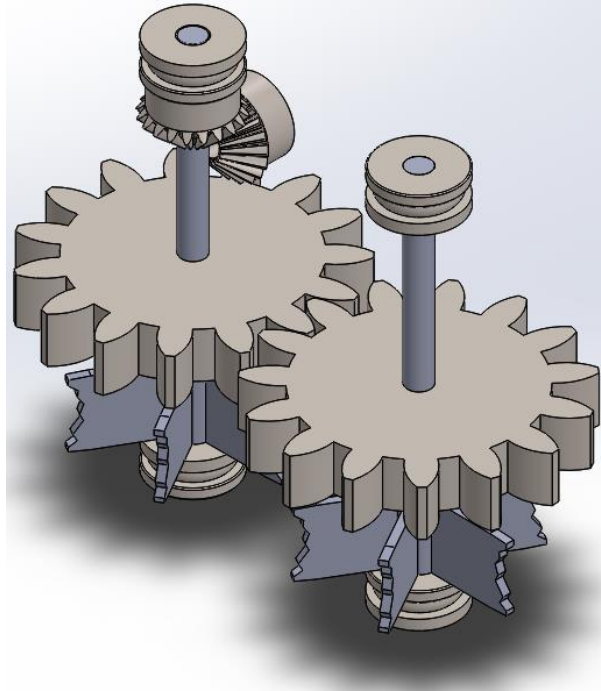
Montaje de Mecanismos con Engranajes Rectos
